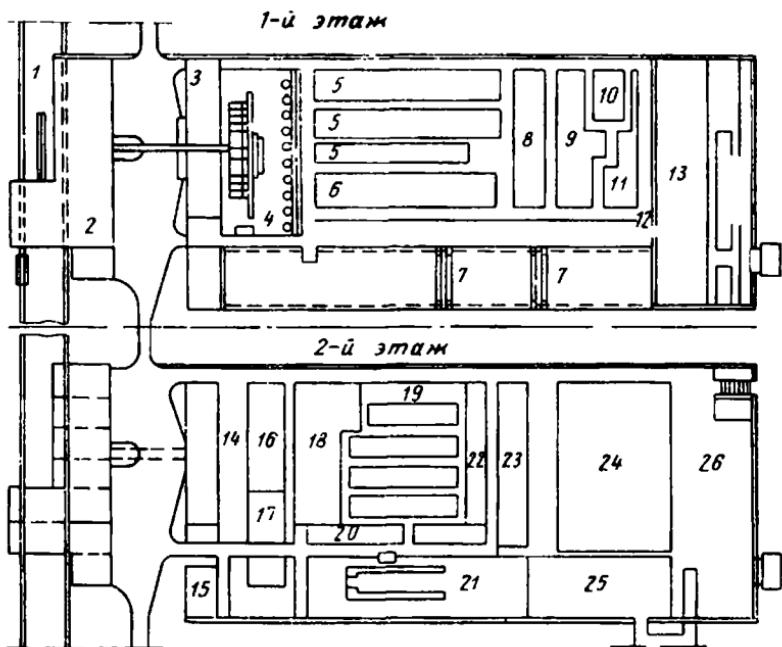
Компоновка цеха ковкого и стального литья фирмы Рено:
